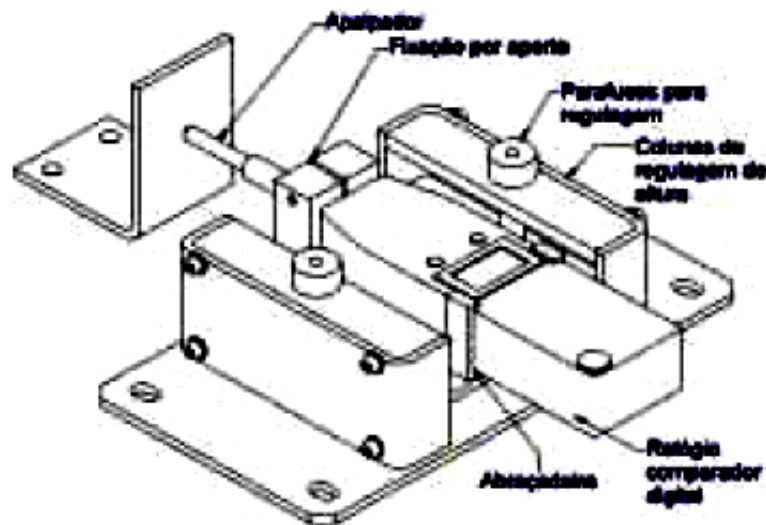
Protótipo desenvolvido por (MORAIS et. al (2003)) para a monitorar fissuras no concreto e deslocamentos entre juntas de barragens de concreto
